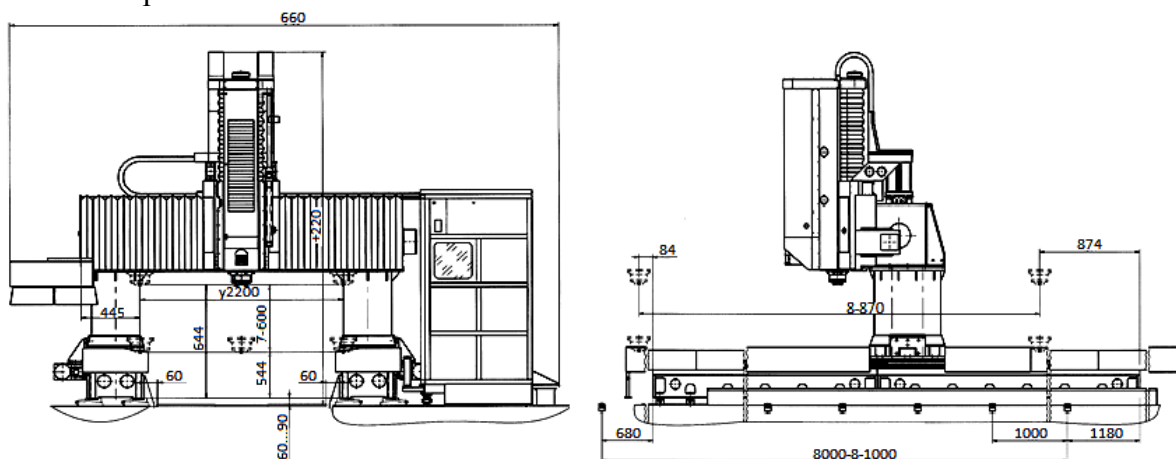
Продольно сверлильно-фрезерный станок МС21ГМФ2-14
